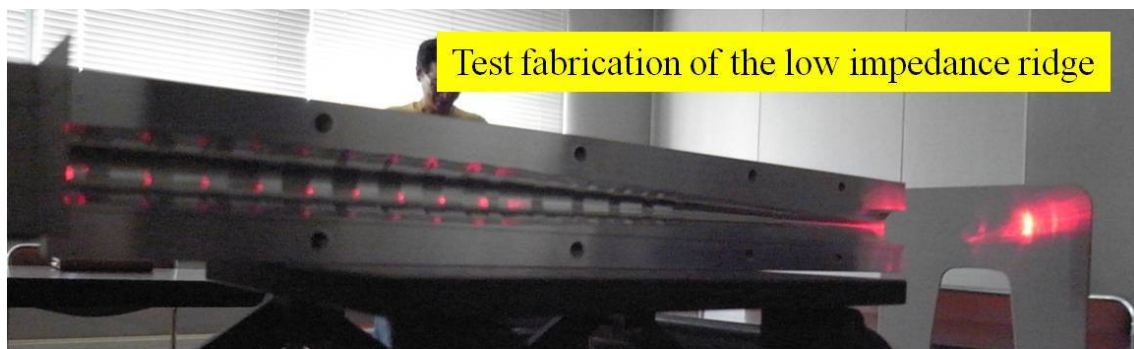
アルミによる ridge 構造のモックアップ (左側から赤色レーザー光を ridge 部分に当てている)
